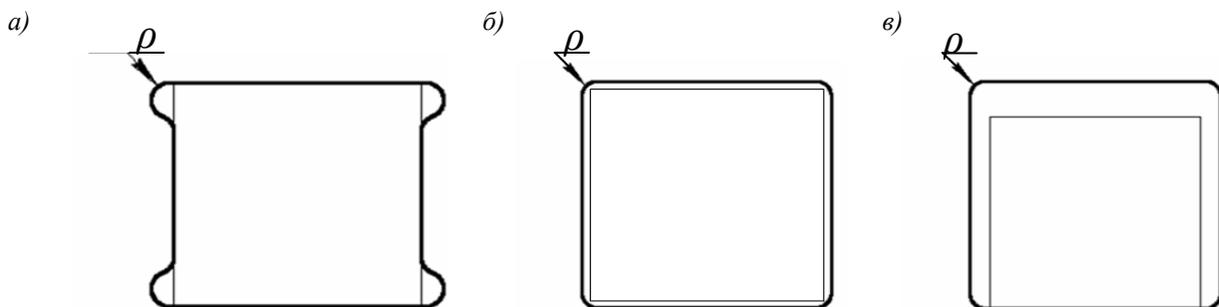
Варианты формирования заготовок для квадратных чистовых БМНП: а) с дополнительными дугвыми выступами, удаляемыми при заточке; б), в) схемы заточки чистовых квадратных пластин без дугвых выступов
